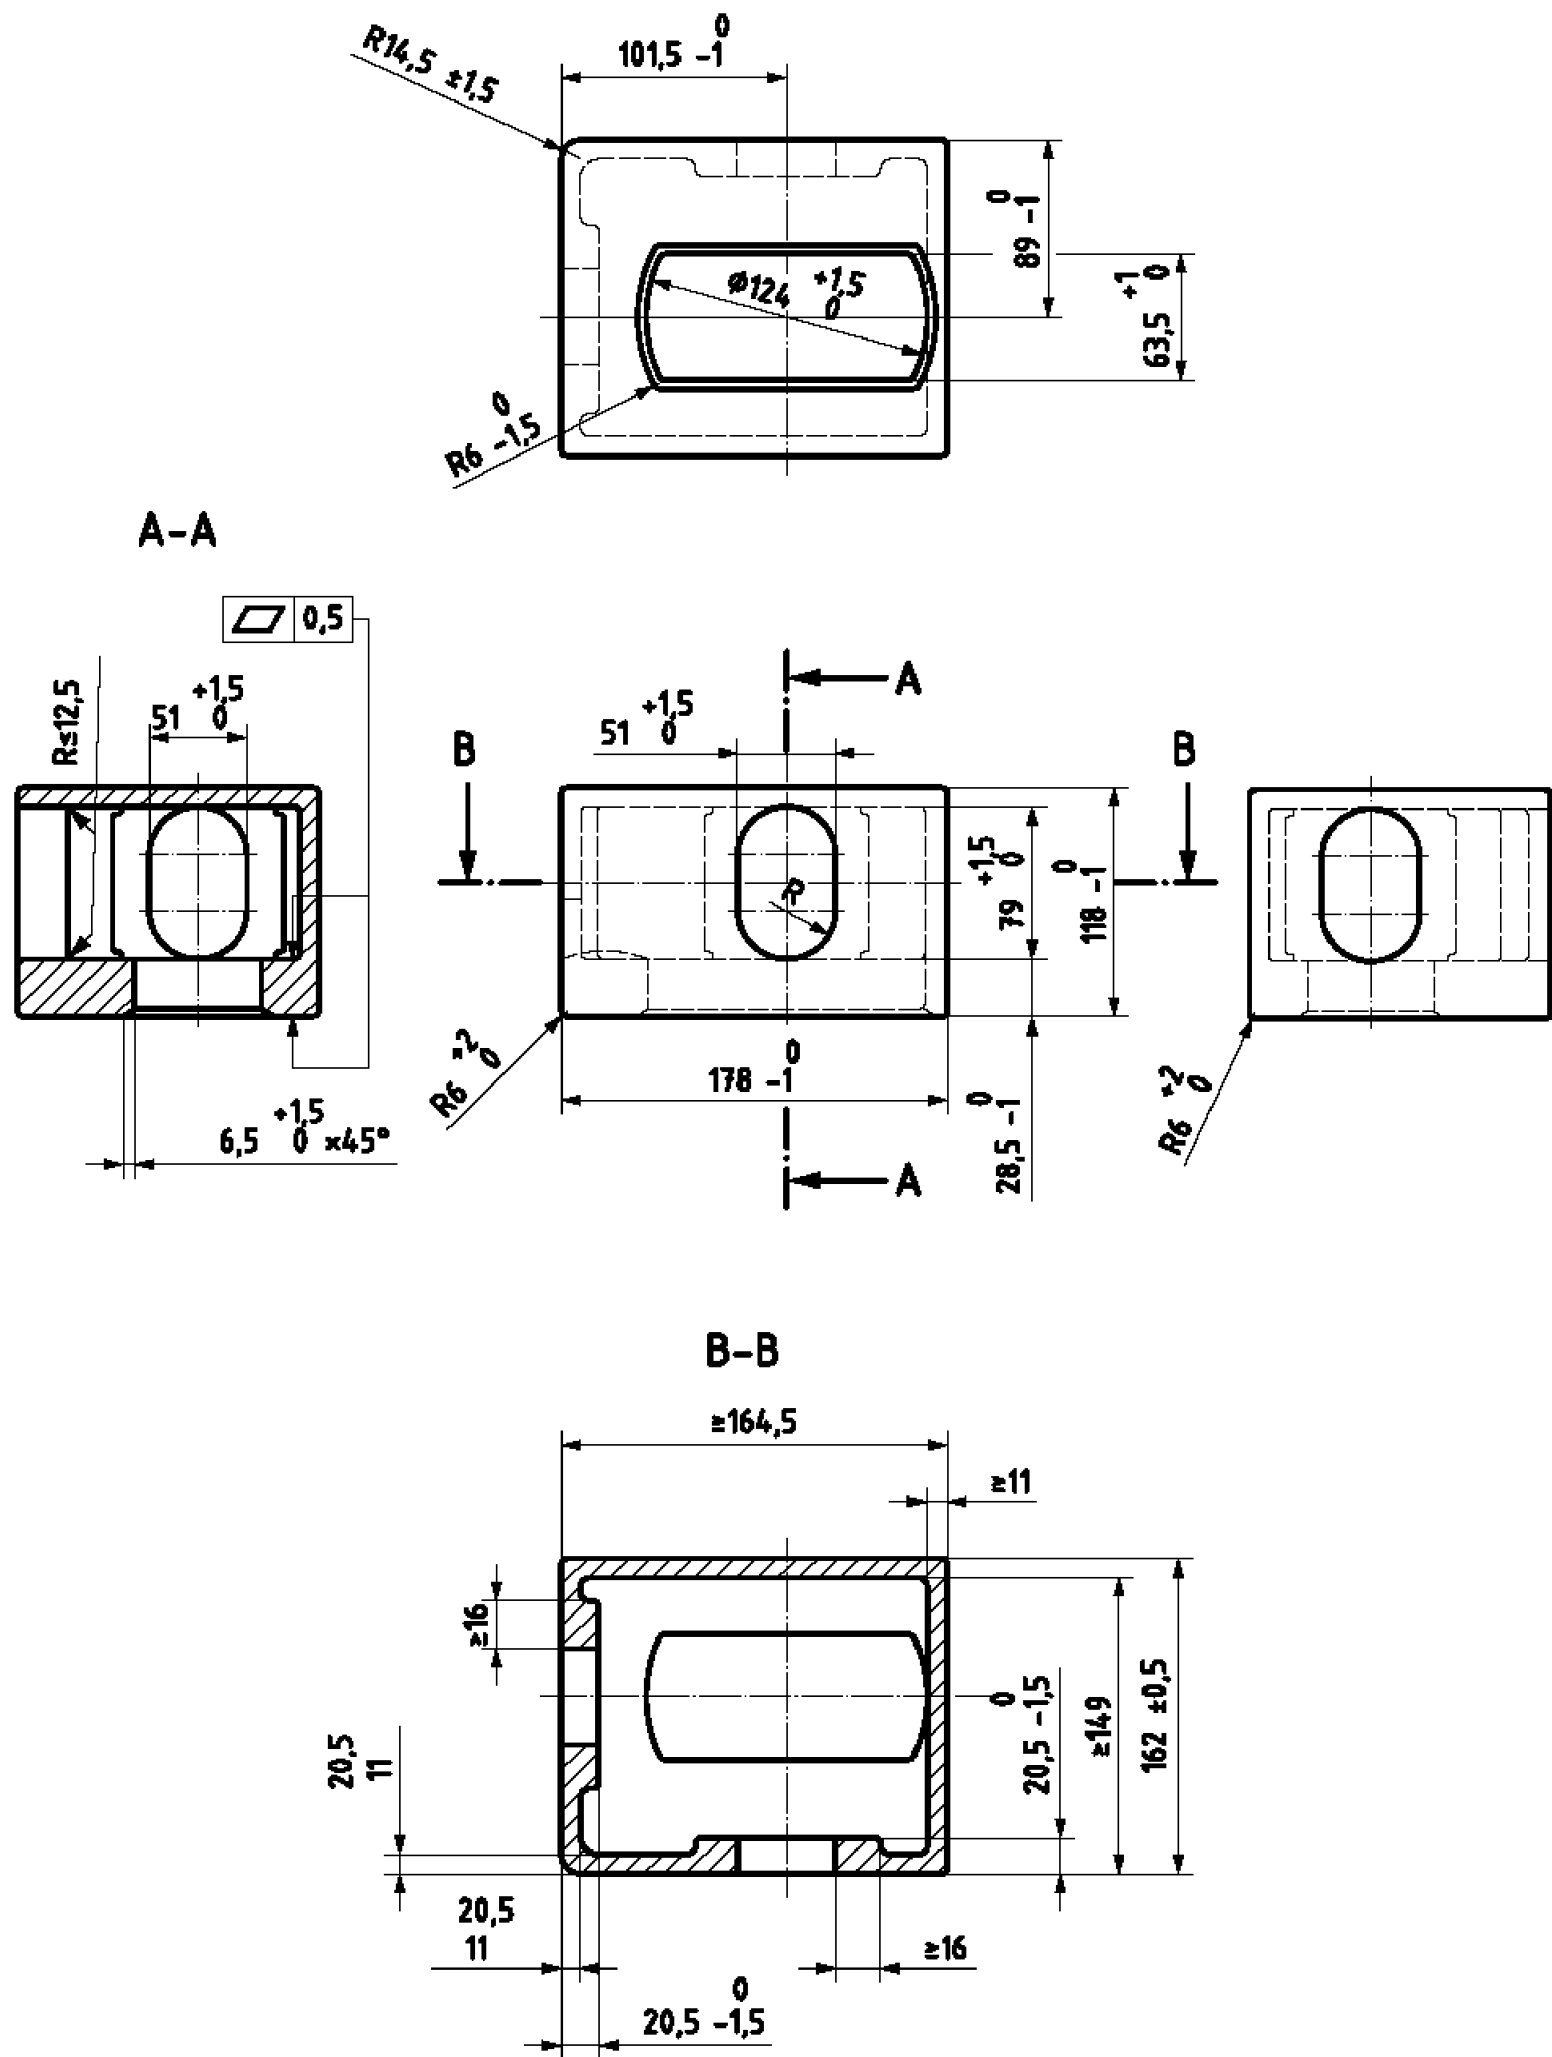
Нижний промежуточный фитинг, мм
